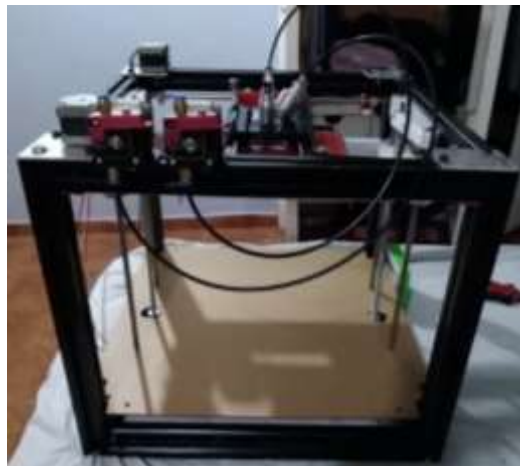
Impresora 3D fabricada en la Universidad Técnica del Norte.
